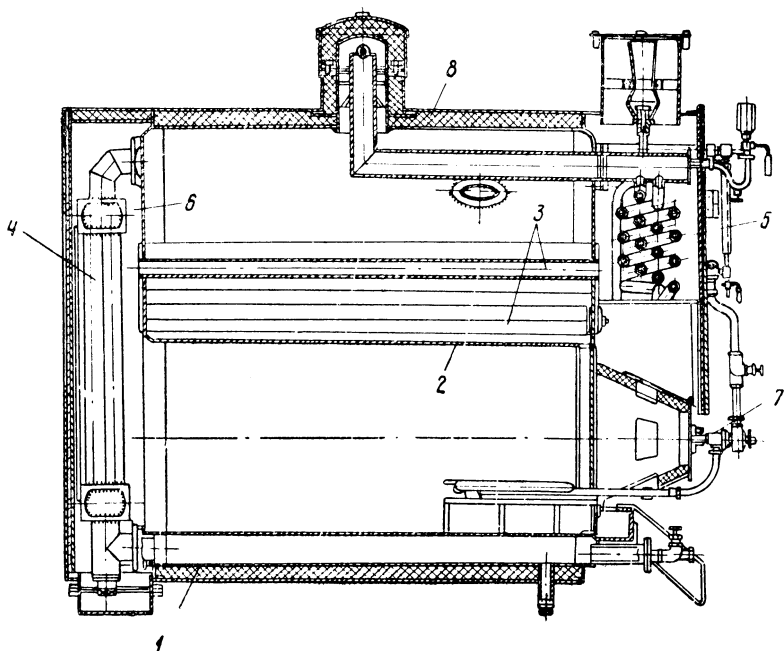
Оборотный котел передвижной котельной установки ППК-51
